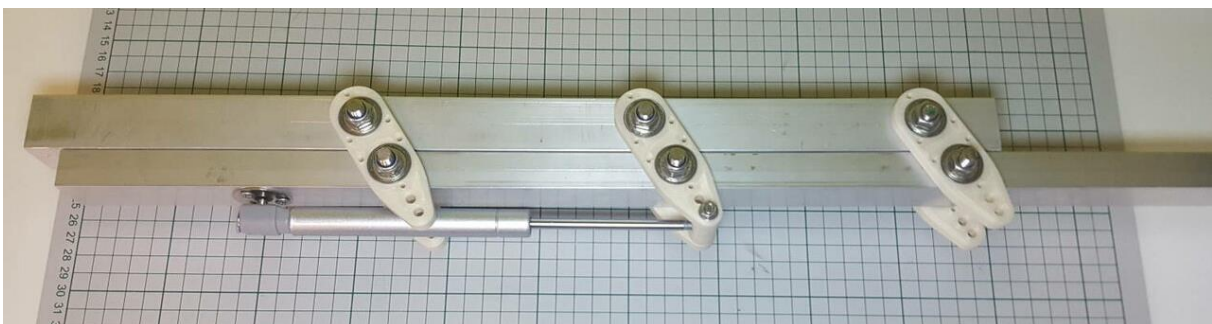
Gefertigter Prototyp meines Auflaufmechanismus
